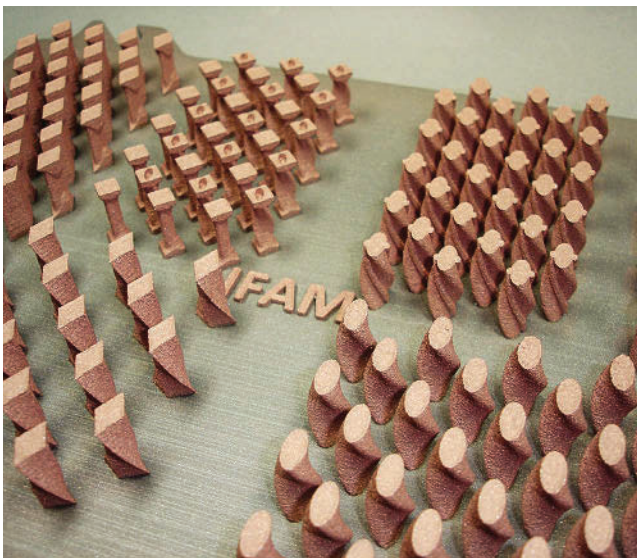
Demonstrator verschiedener Kühlstrukturen aus Reinkupfer auf Edelstahl-Grundplatte.
